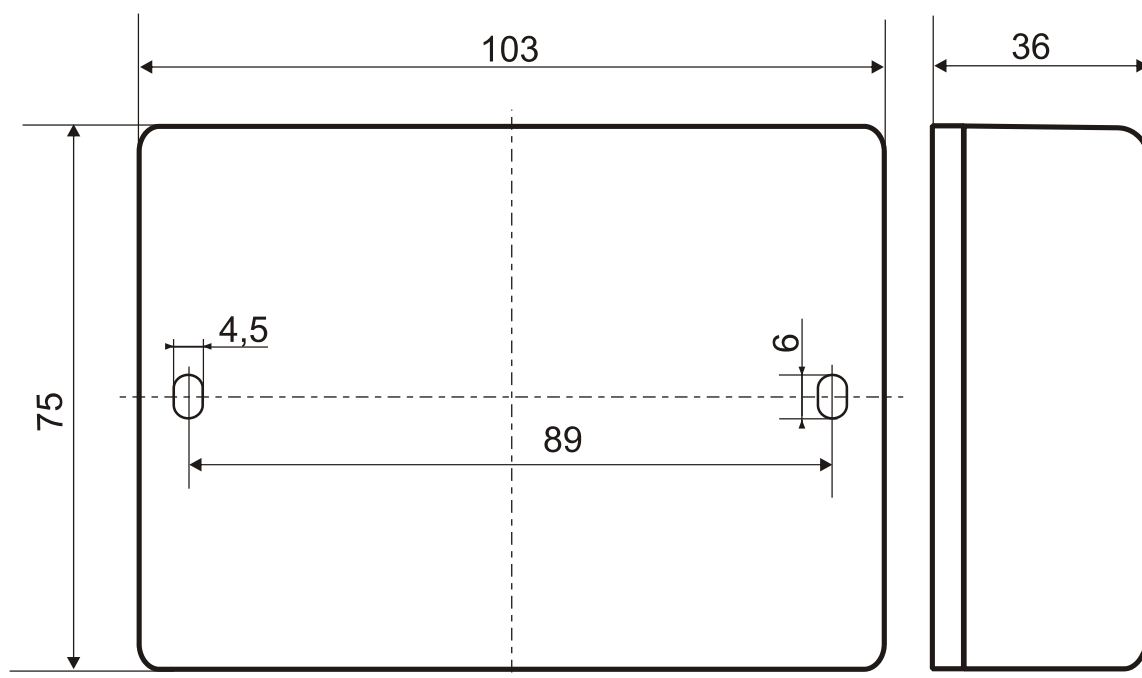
Габаритные и установочные размеры SF-CM-1
